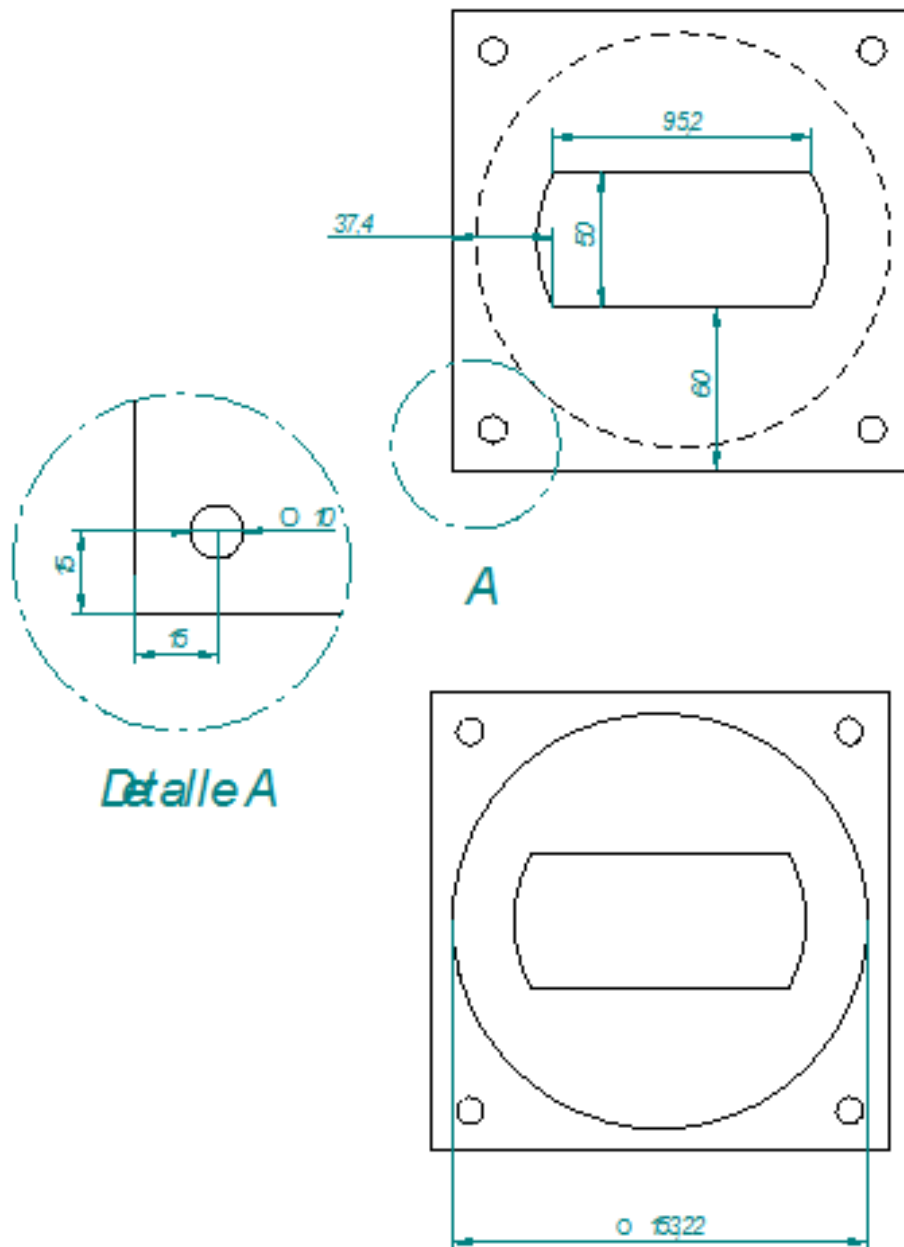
Plano de Cuerpo de vidrio. A) Vista Superior B) Vista Inferior.
